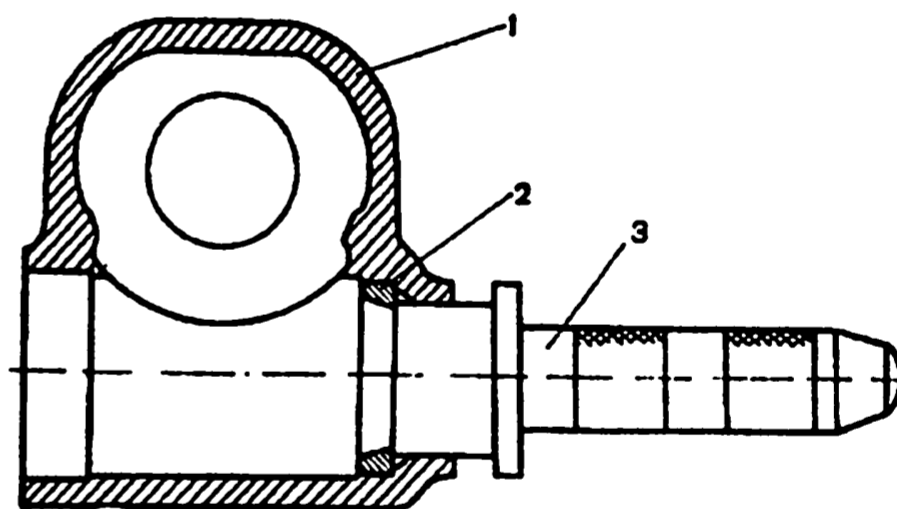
Снятие наружного кольца верхнего подшипника червяка с помощью оправки 67.7853.9541: 1 - картер рулевого механизма; 2 - наружное кольцо верхнего подшипника червяка; 3 - оправка 67.7853.9541
